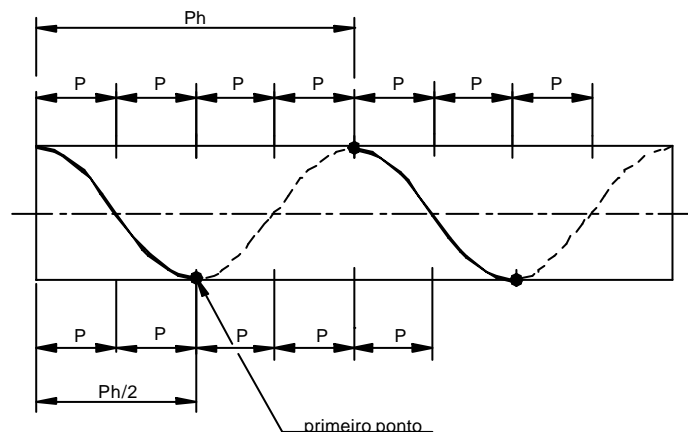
Primeiro ponto para o traçado da rosca
